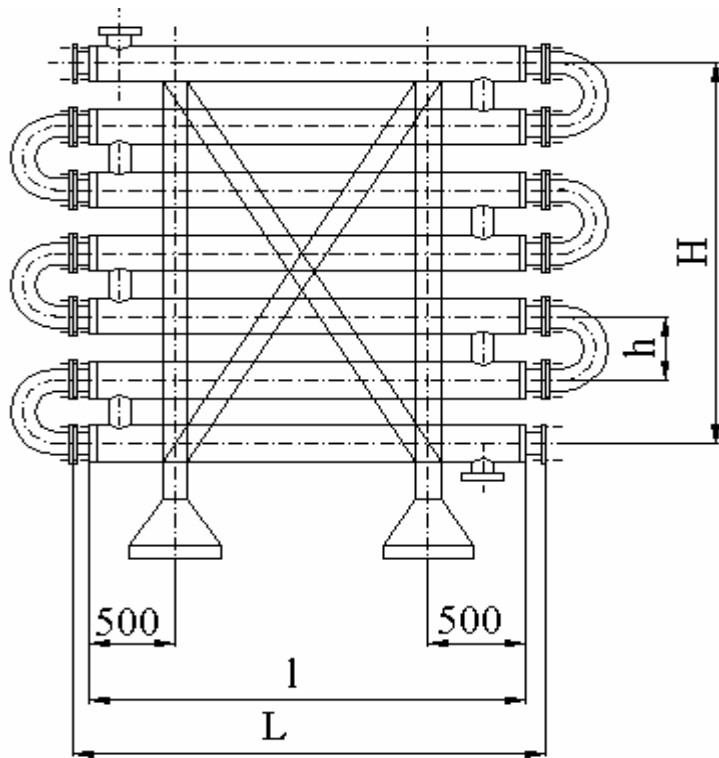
Сборочный чертеж теплообменника типа ТТ
